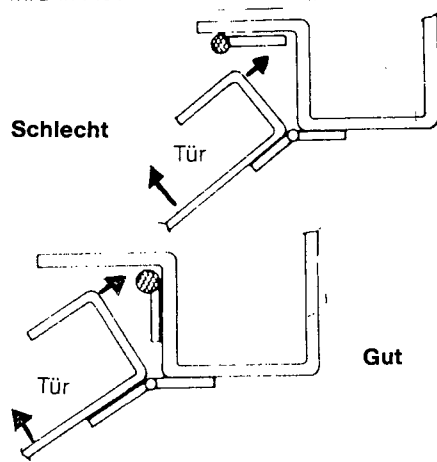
Dichtungskonstruktionen in einer beweglichen Verbindung
